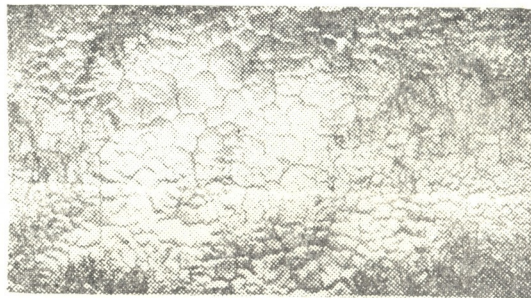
Сетка разгара на дне I калибра клетки 900 трубозаготовочного стана 900/750×3
